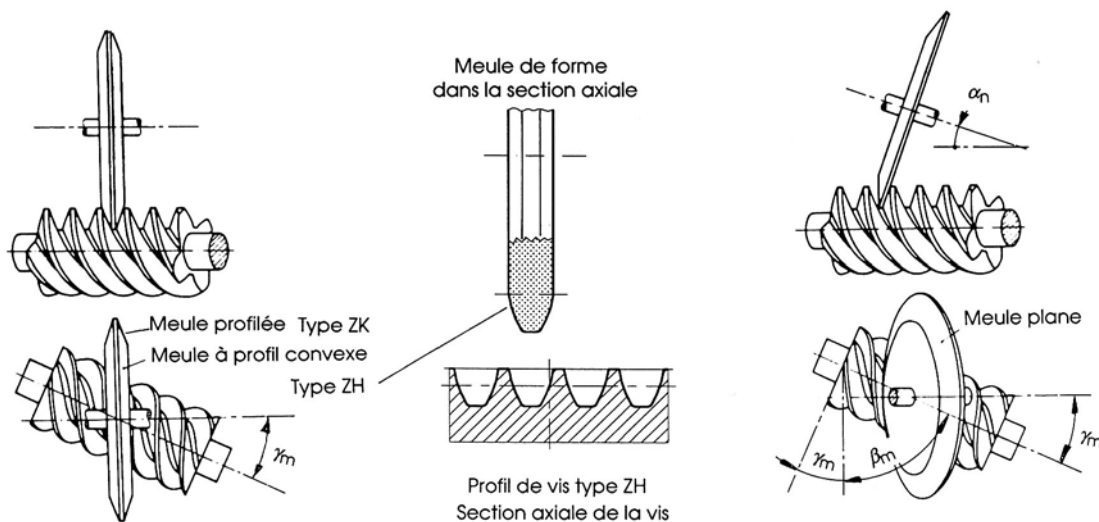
Définition et fabrication des flancs de la vis : vis de types ZK, ZH et ZI
